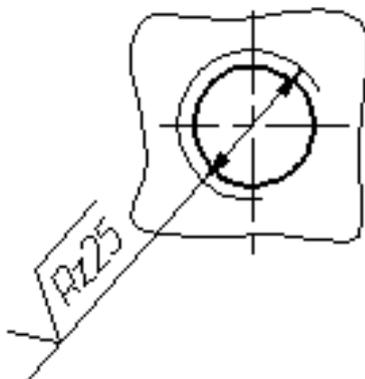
Обозначения шероховатости внутренней резьбы на продолжении размерной линии
